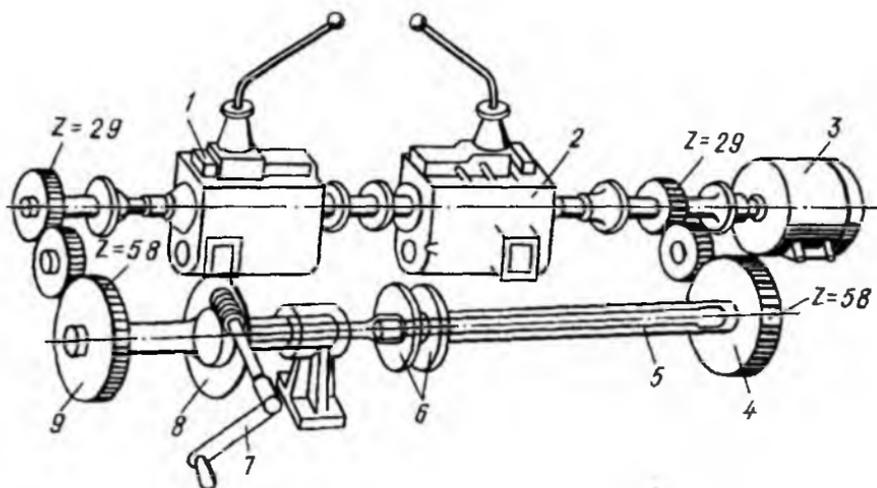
Схема стенда для обкатки коробок передач с замкнутым методом нагружения:
